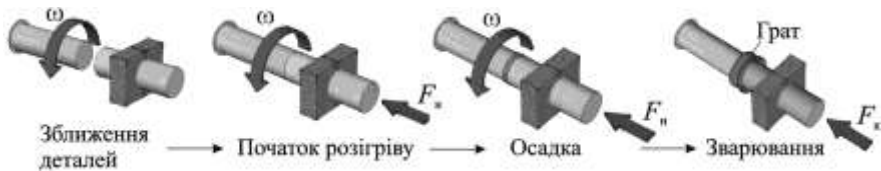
Етапи конвекційного зварювання тертям
